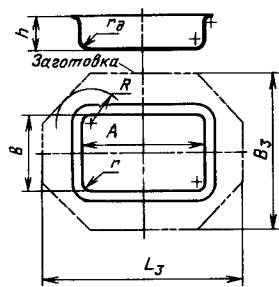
Упрощенный способ построения контура заготовки при вытяжке коробчатой детали
